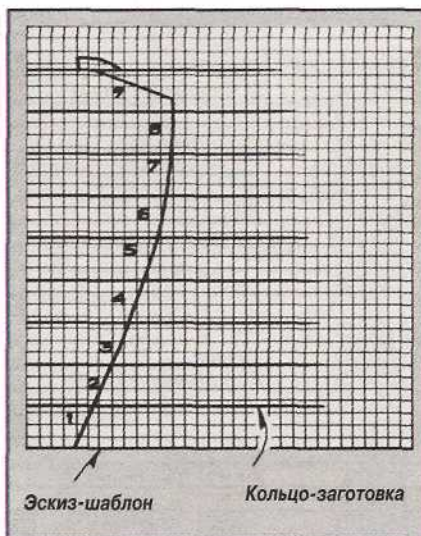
Эскиз-шаблон внешних обводов корпуса вазы.
